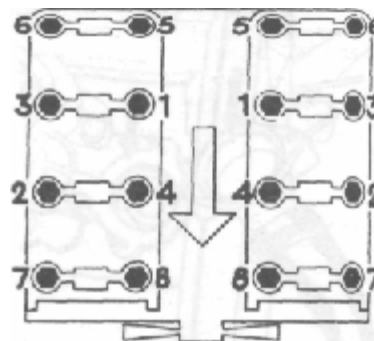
Порядок затяжки болтов крепления коромысел. Отворачивание производится в обратном порядке — Двигатель B280F
